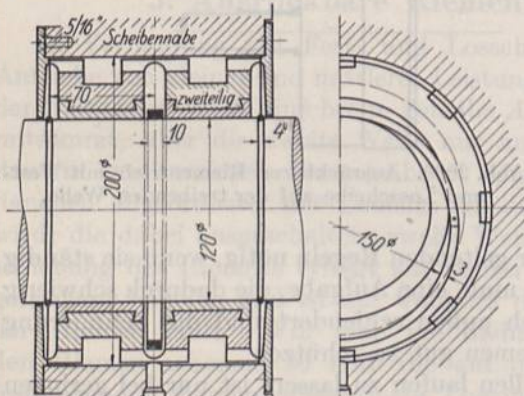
Leerlaufbüchse mit Ringschmierung. Prager Maschinenbau-A. G. M. 1:5.
